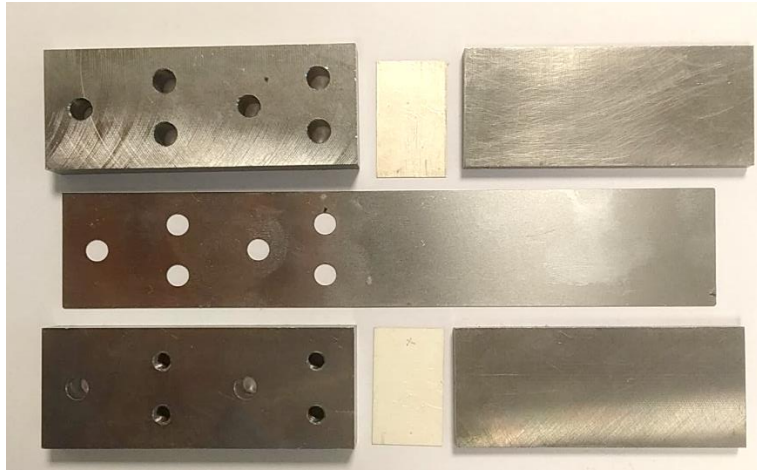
Photographie des éléments du prototype PZT W avant assemblage
